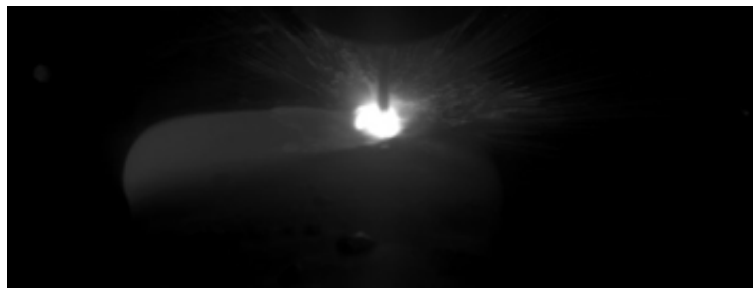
Bild aus dem Schweißprozess bei Gefertec
